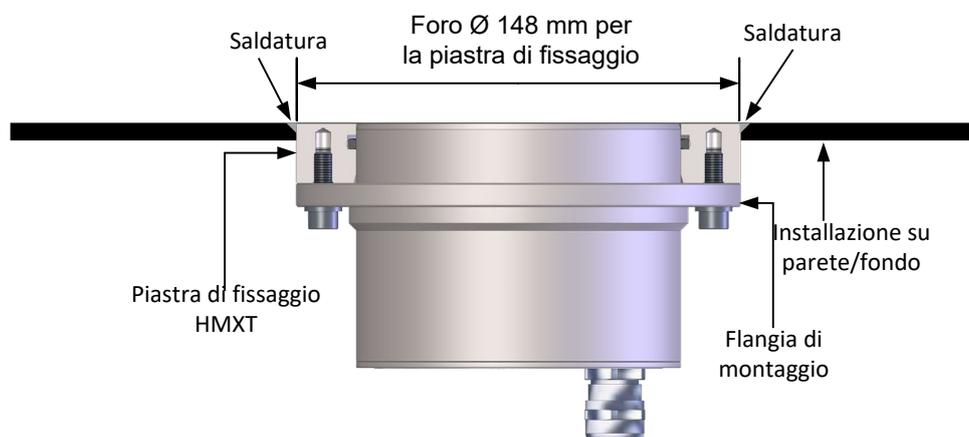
Installazione del sensore (piastra di fissaggio montata a filo)
